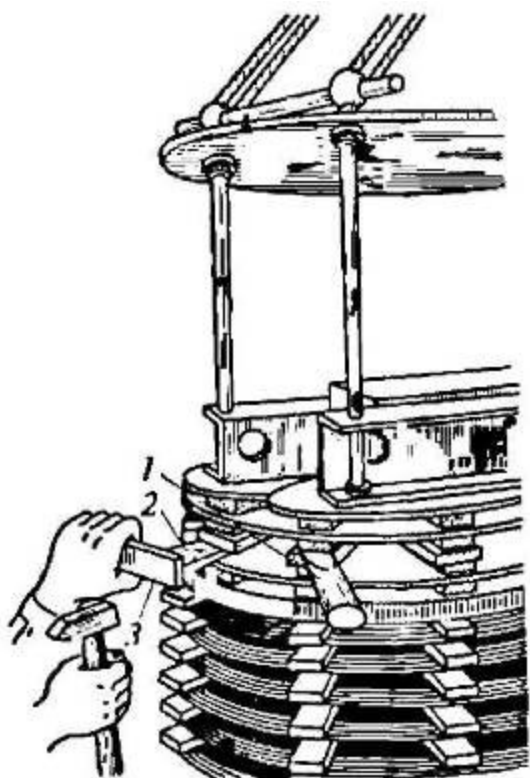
Расклиновка обмотки трансформатора прессующими клиньями: 1-вспомогательный клин;2-дополнительный деревянный клин; 3-деревянный брусок
